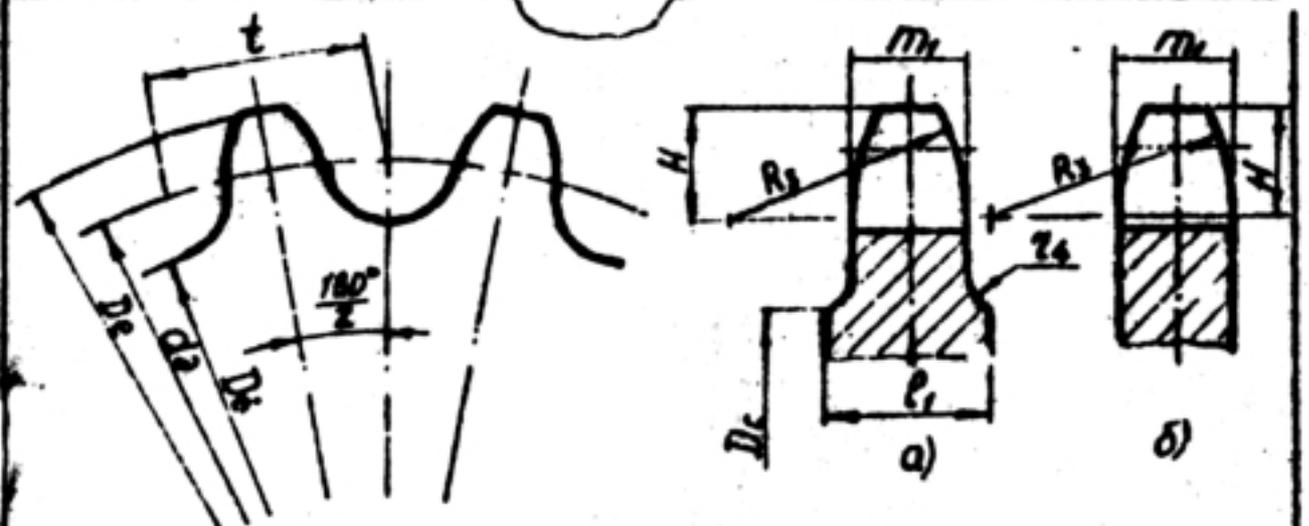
Звездочки конического колеса (по ГОСТ 504-69)
